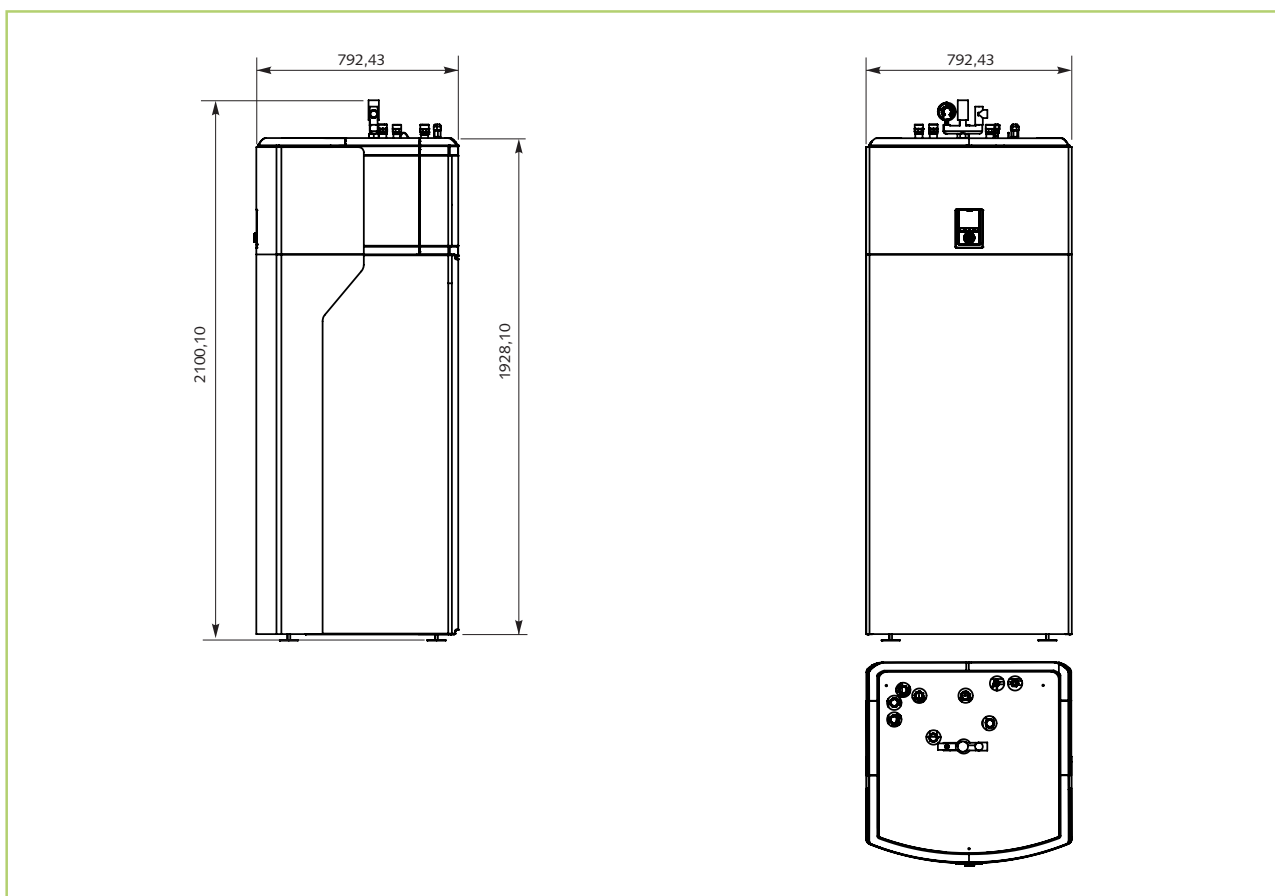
Abmessungen Innenmodule WKF-compact 85/120/180
